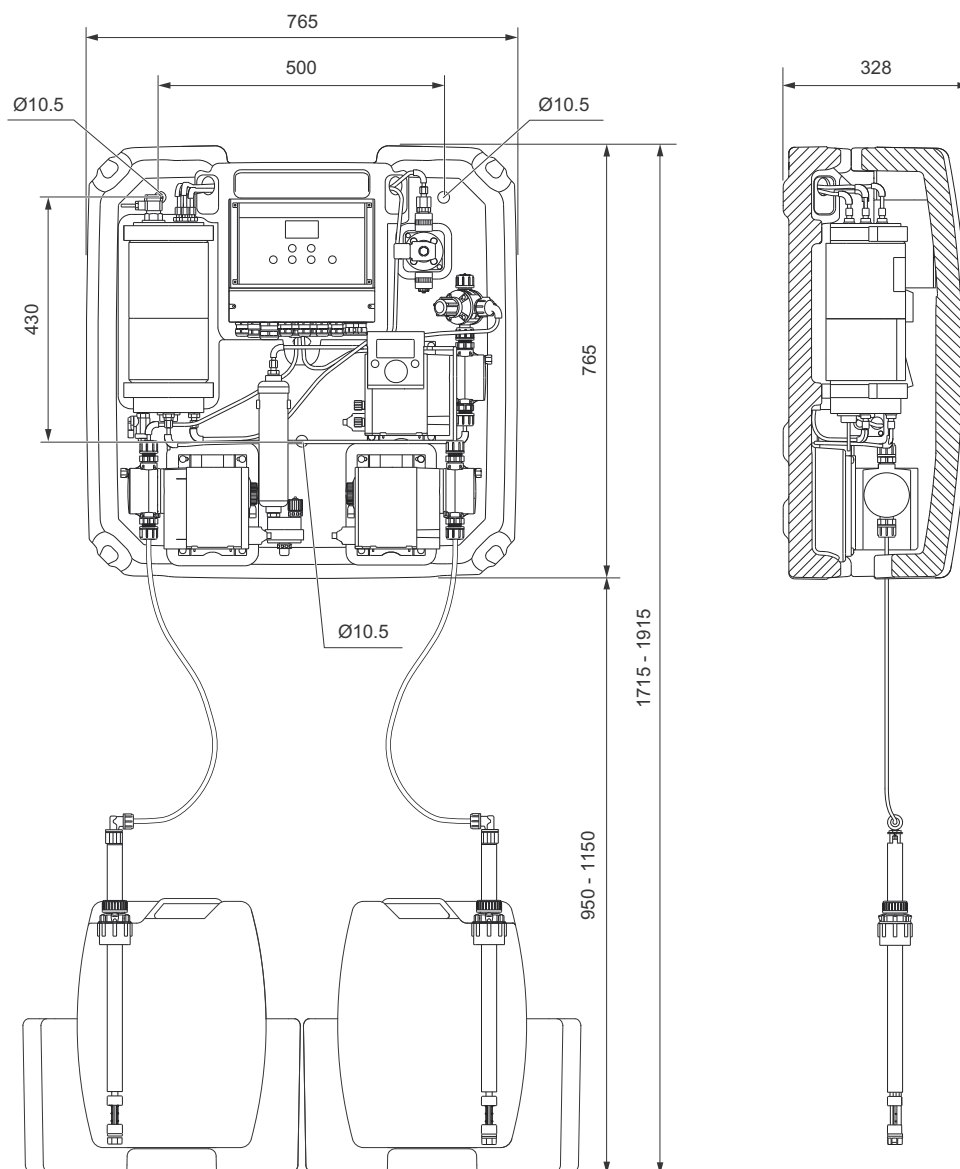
Габаритные размеры установки Oxiperm Pro OCD-162-5 и OCD-162-10, с указанием отверстий для крепления
